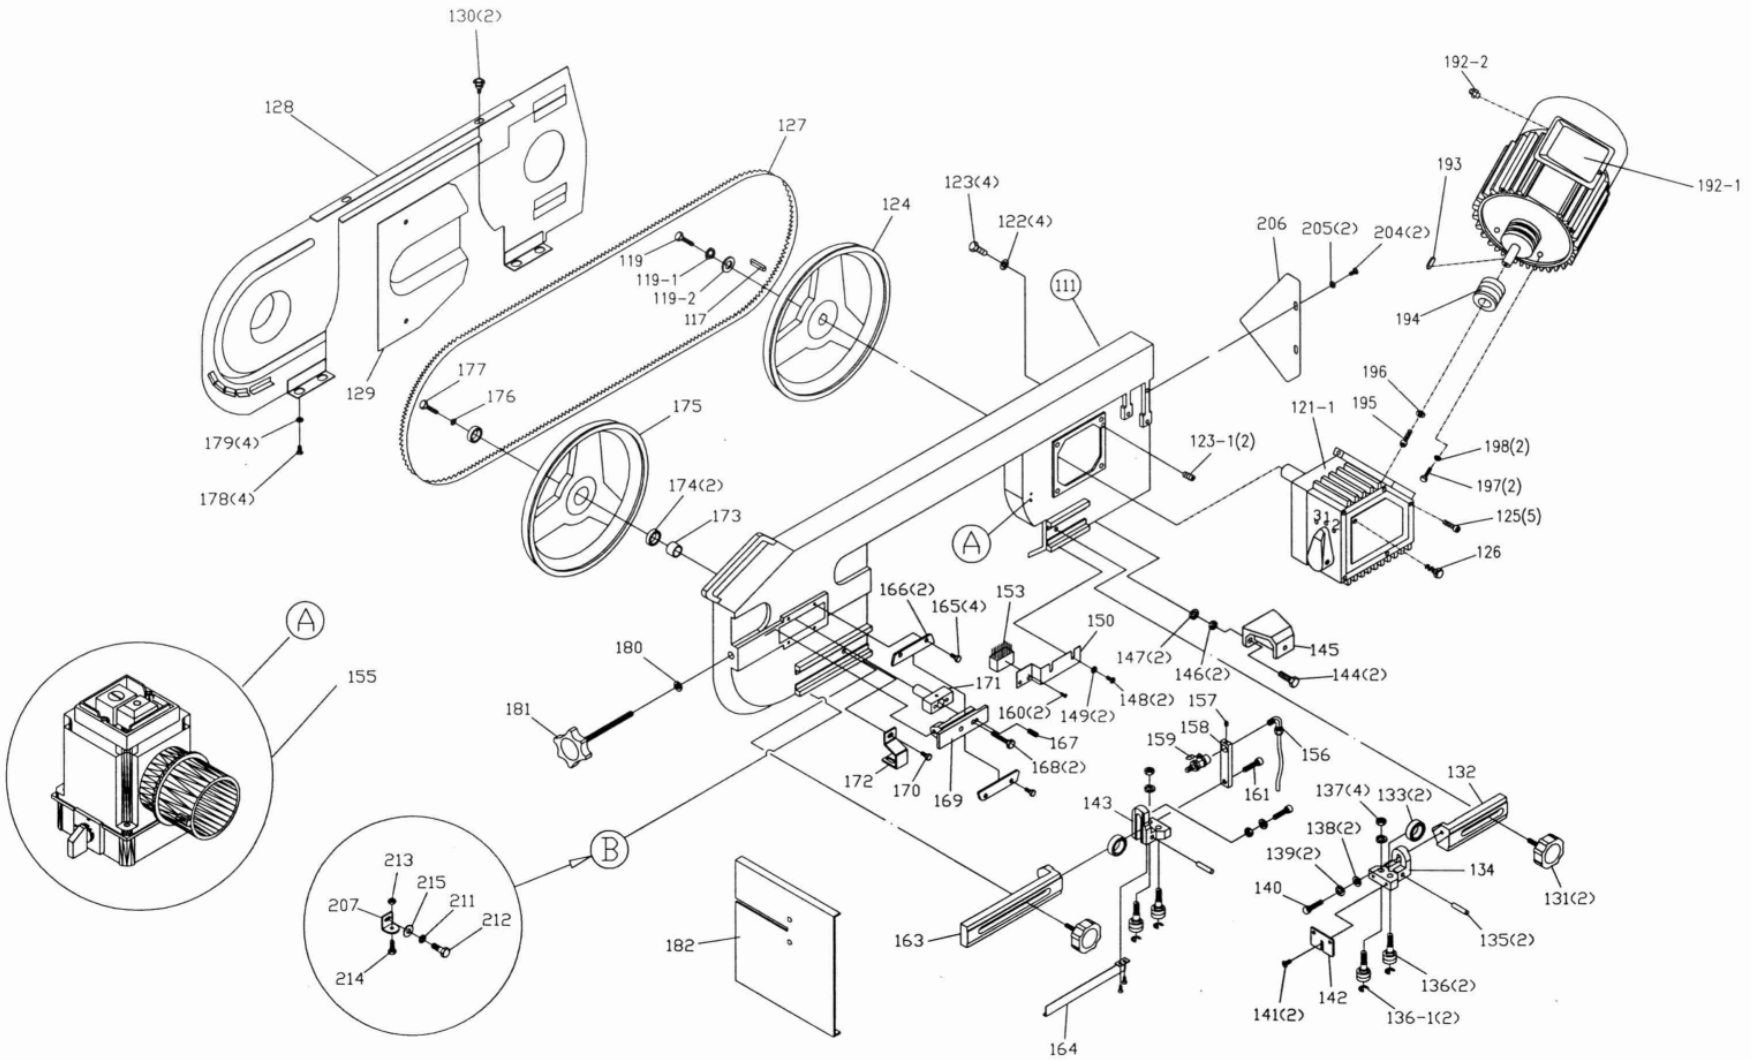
Explosionszeichnung - Explosion drawing 2
